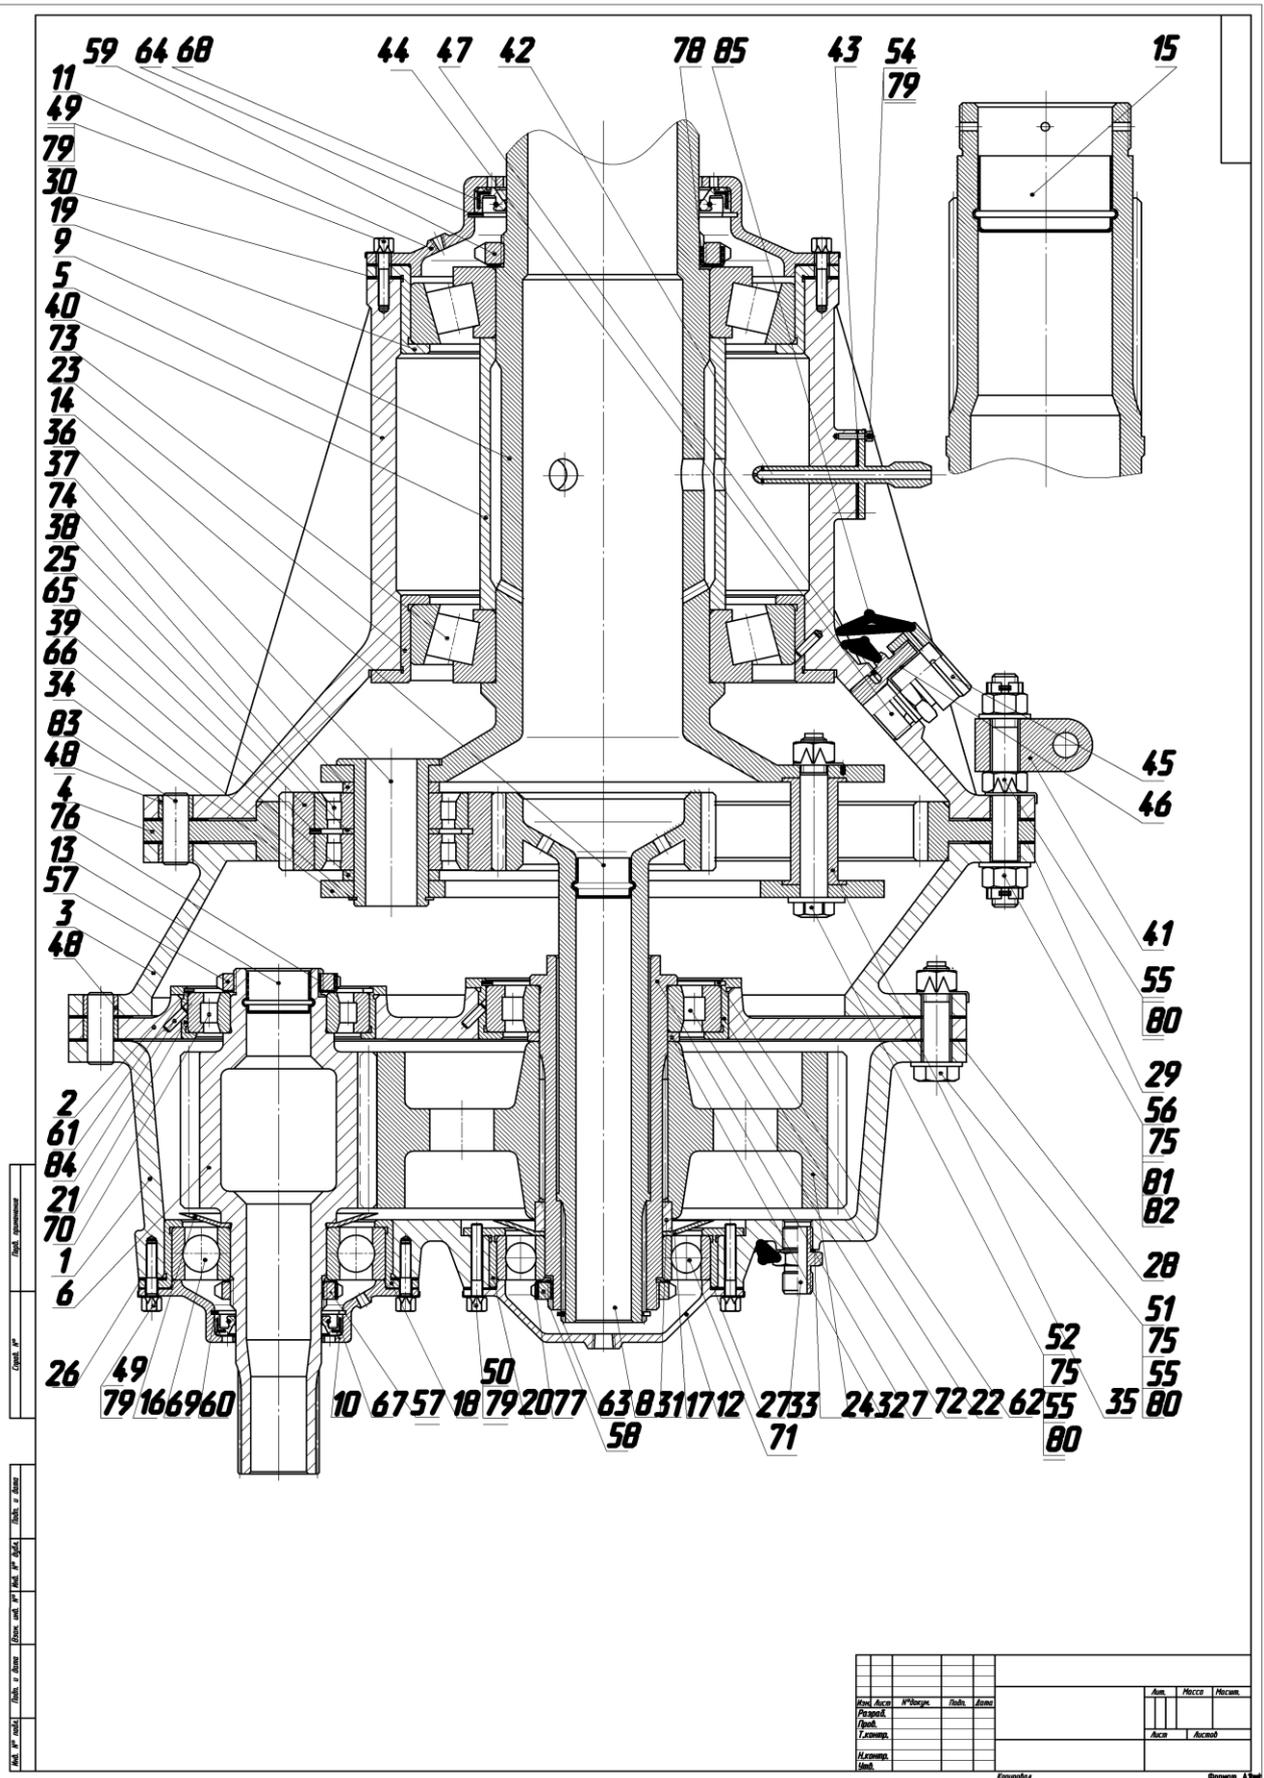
Фрагмент чертежа общего вида редуктора – продольный разрез и позиции
